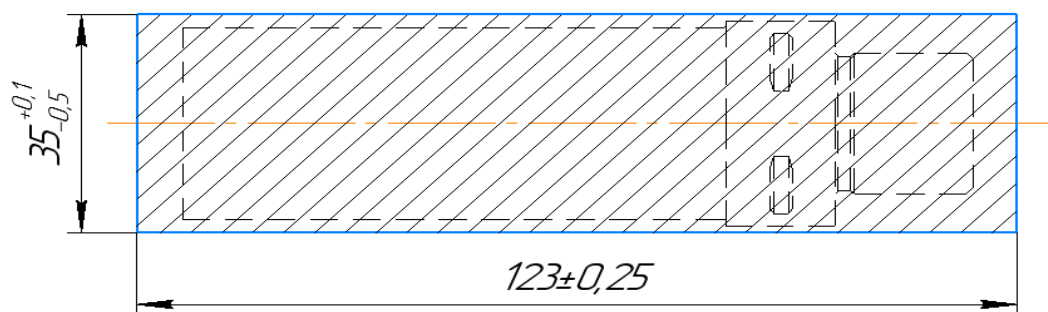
Заготовка хвостовой части режущего инструмента
